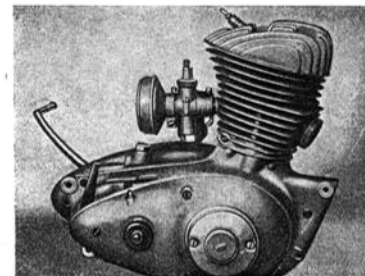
Triebwerkblock Typ RT 125, Lichtmaschinen-seite
